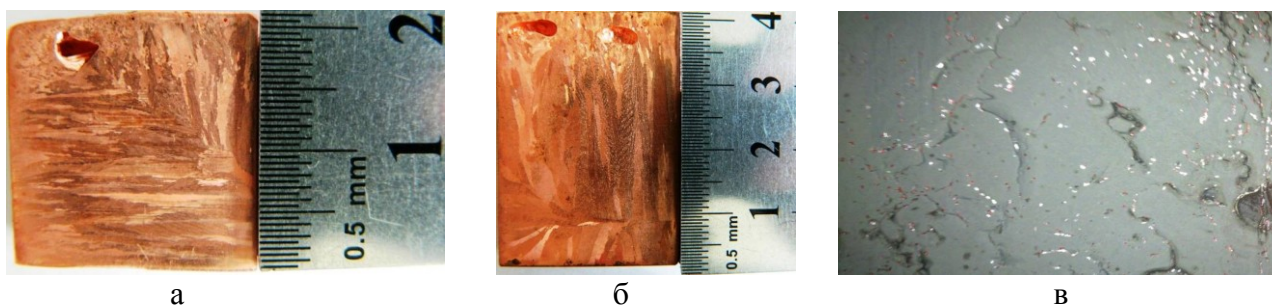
Крупные газовые поры (а, б) в верхней части поперечного сечения литой заготовки; неслитины (в) на нижней поверхности литой заготовки
